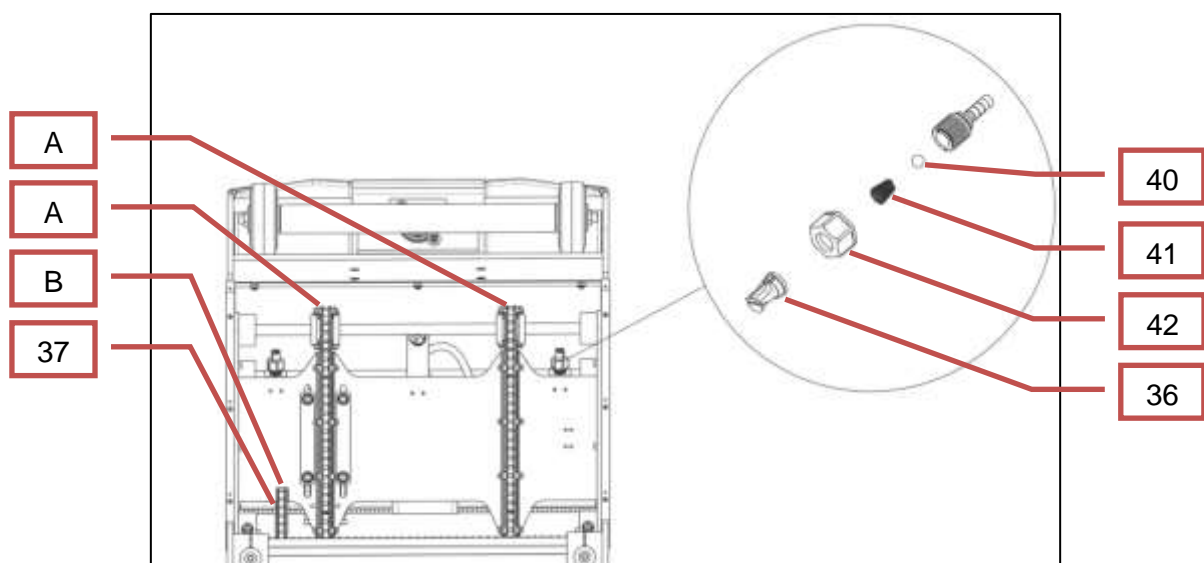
Accionamiento por cadena / boquillas pulverizadoras
